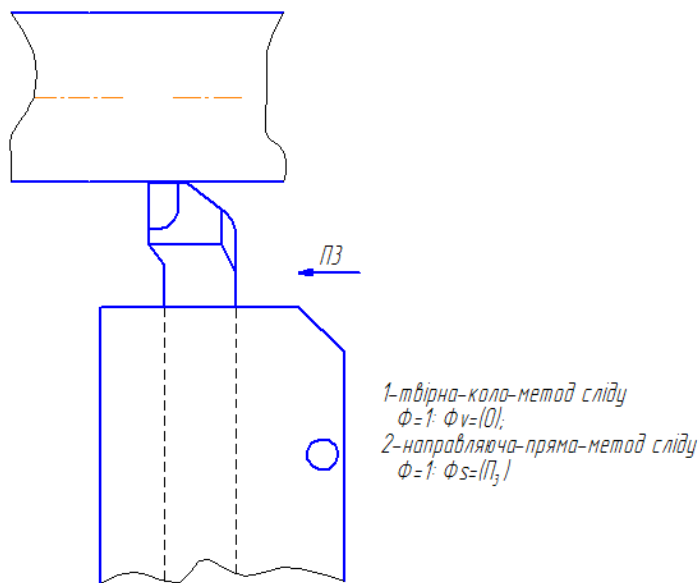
Комплекс формоутворюючих рухів при обертovому русі заготовки та поступальному руху інструменту (операція точіння)
